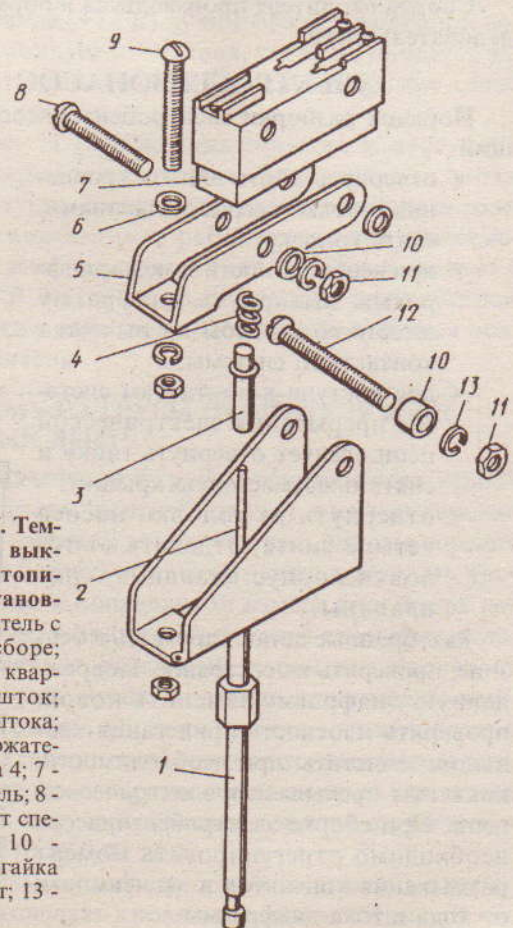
Температурный выключатель отопительной установки: 1 - держатель с трубкой в сборе; 2 - стержень кварцевый; 3 - шток; 4 - пружина штока; 5 - скоба держателя; 6 - шайба 4; 7 - переключатель; 8 - винт; 9 - винт специальный; 10 - втулка; 11 - гайка М4; 12 - винт; 13 - шайба 4Т
